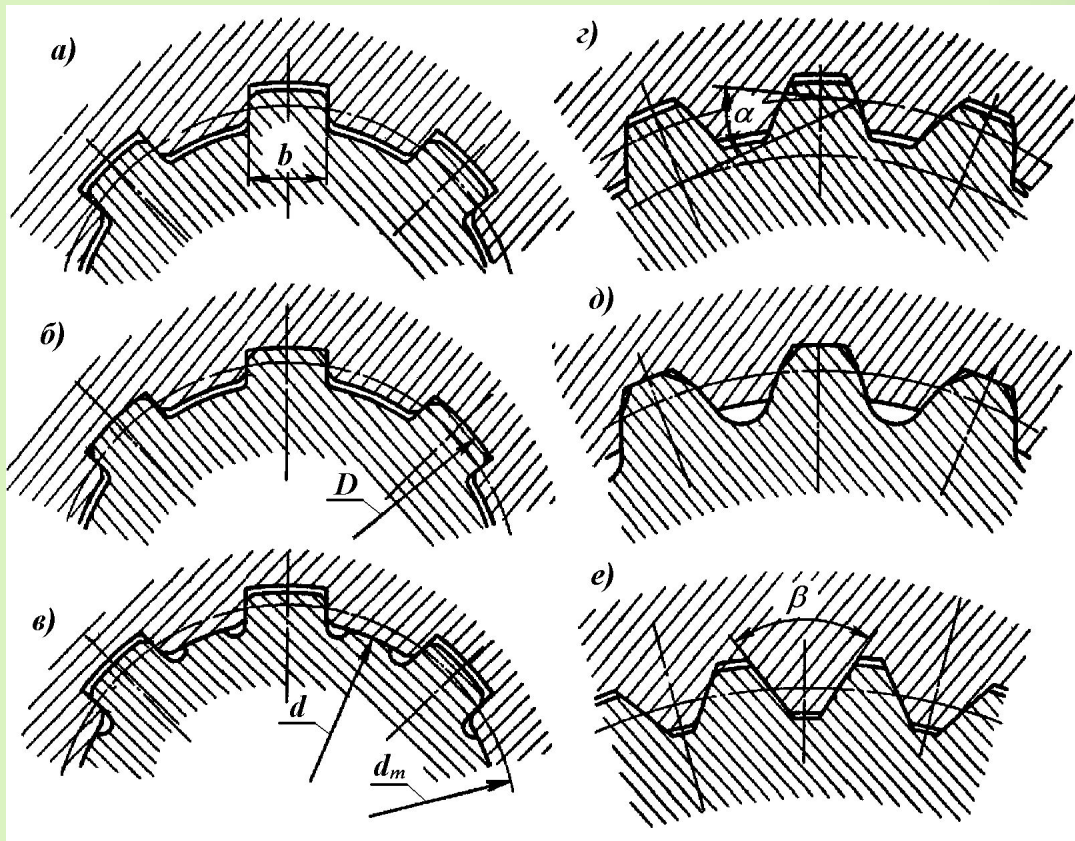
Типы и центрирование зубчатых (шлицевых) соединений:
